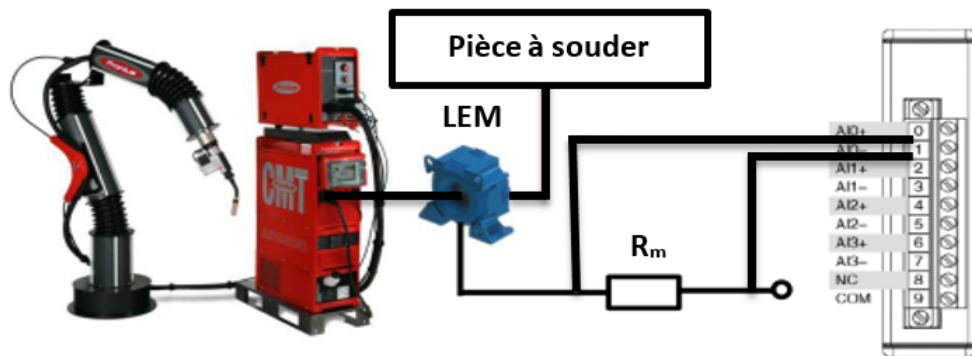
Montage électrique utilisé pour l'acquisition de l'intensité de soudage.
